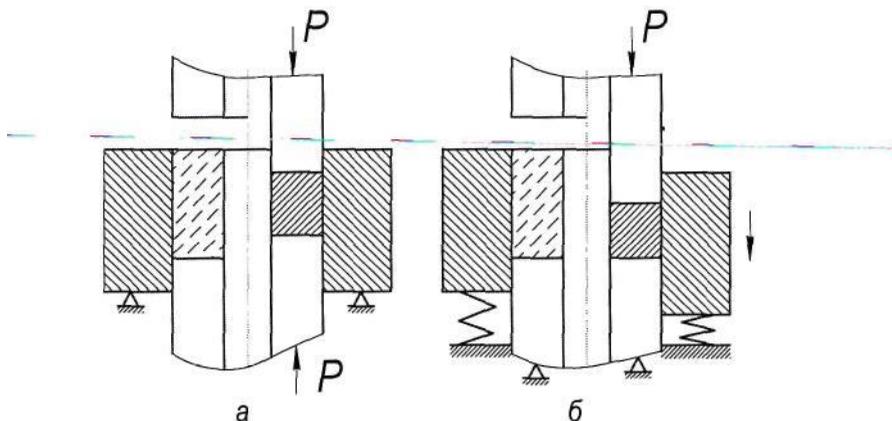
Схемы двустороннего прессования: а– с неподвижной матрицей; б– с плавающей матрицей
